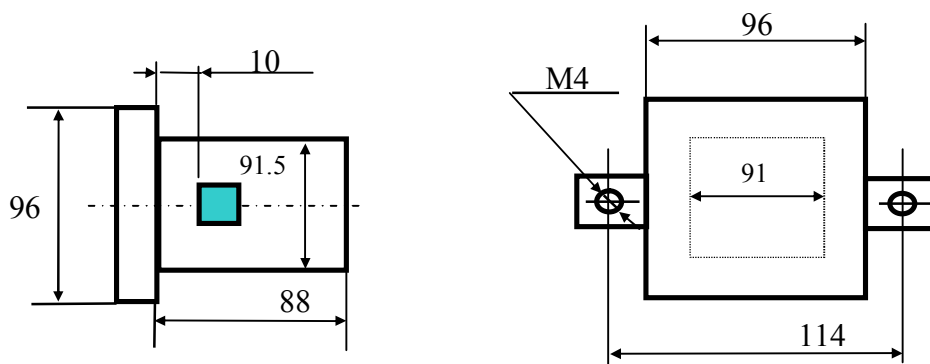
в Габаритные размеры, корпус 96x96x96 мм.
